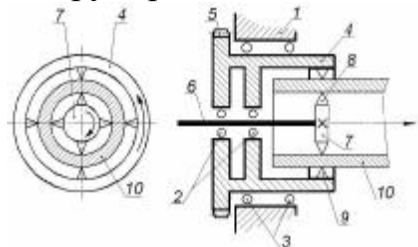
Пристрій для обробки кінців труб, де 1 корпус, 2 і 3 підшипники, 4 фрезерна головка, 5 зубчастий вінець, 6 приводний вал, 7 ріжуча головка, 8 і 9 ріжучі елементи, 10 труба
